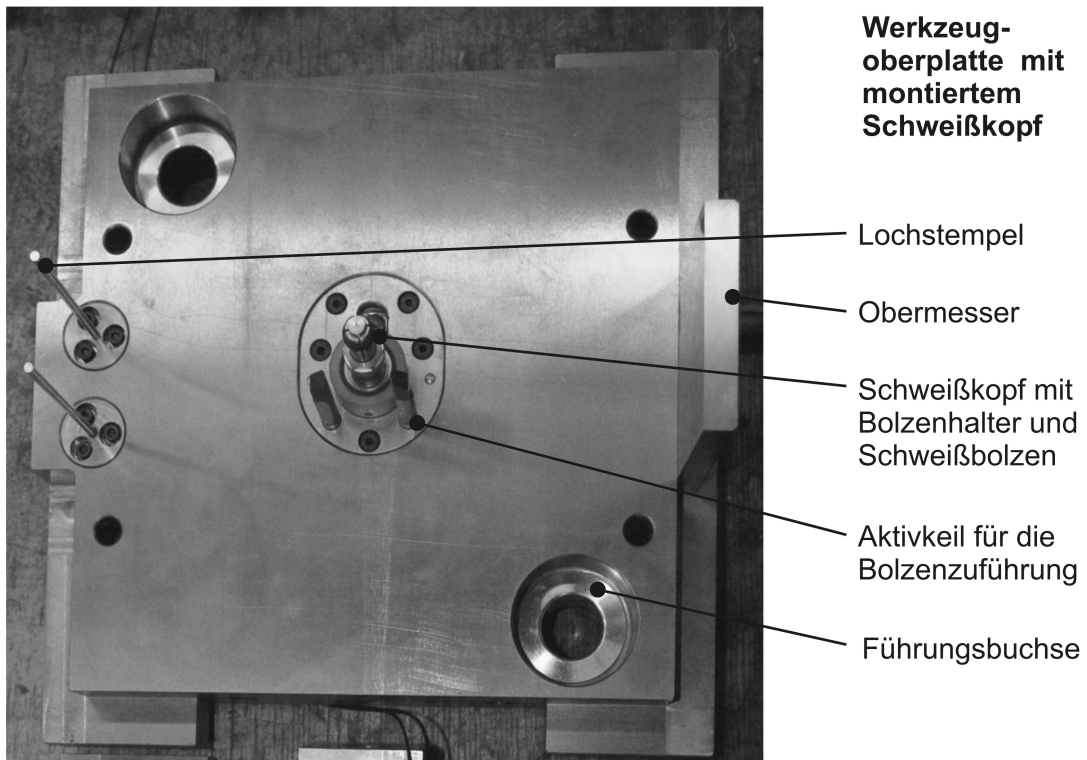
Oberplatte mit montiertem Schweißkopf
